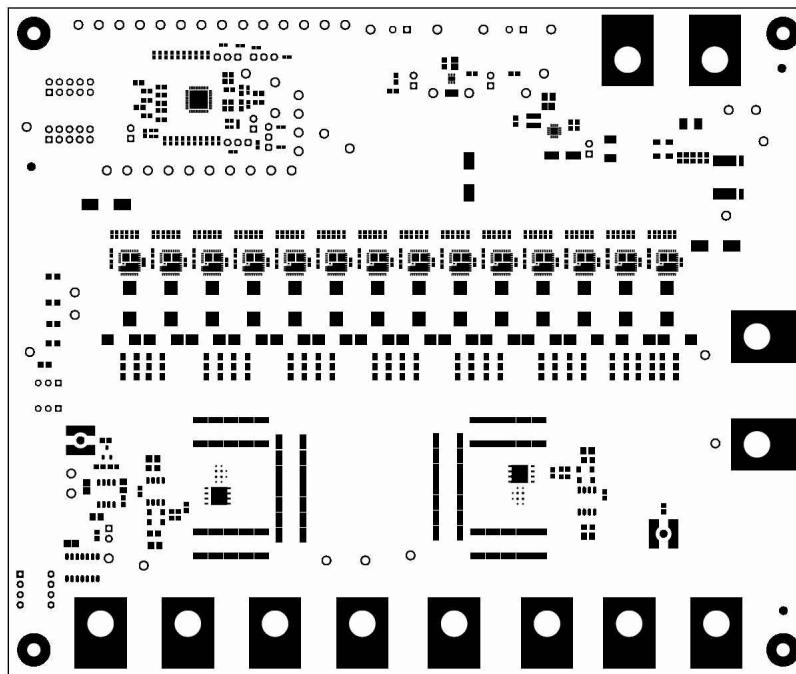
TPS53676EVM-084 PCB 顶部焊接
